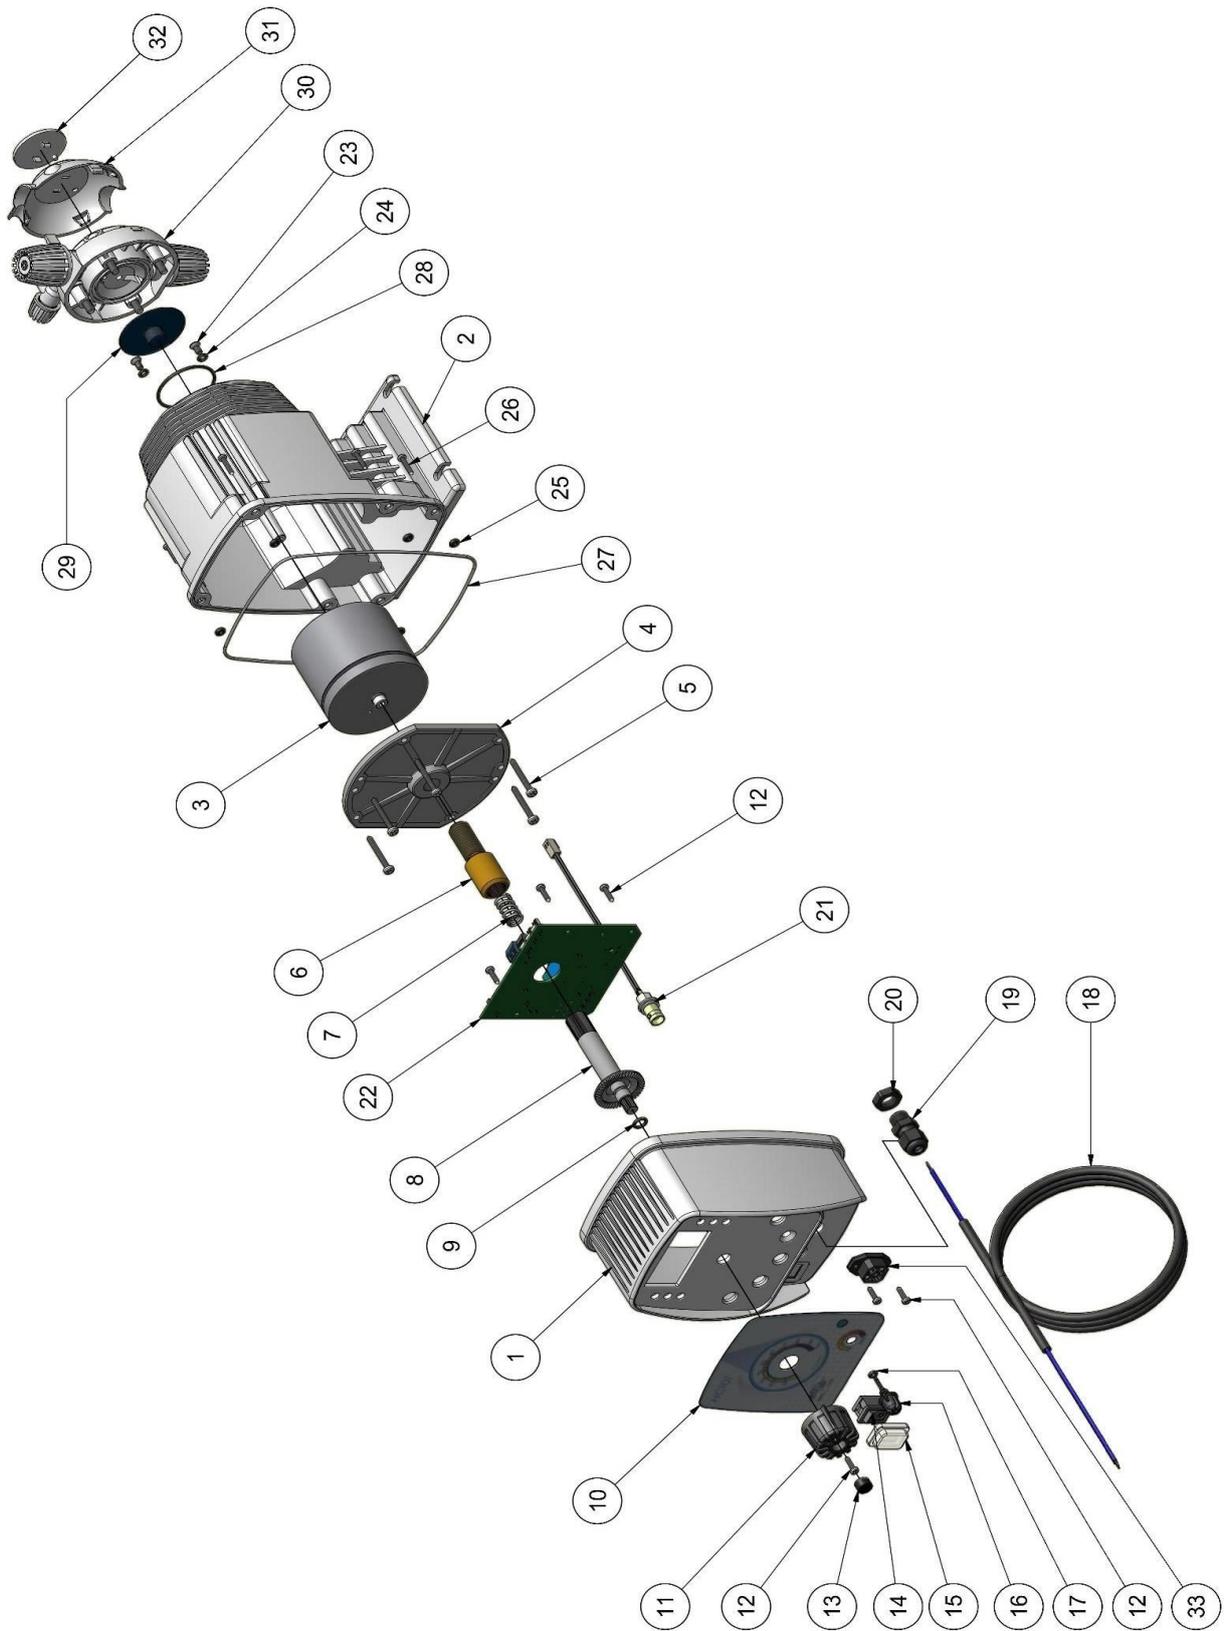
A: HC101 Esploso / Exploded view / Explose / Dibujo / Explosionszeichnung
